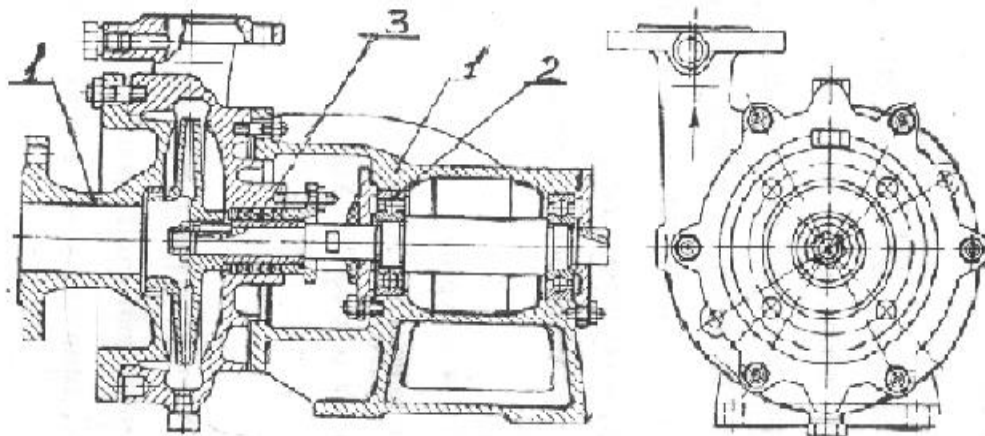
Общий вид центробежного насоса (гидравлической машины) в разрезе: 1) корпус насоса и его крышка (разъемная деталь). Детали заменяемые при текущем ремонте: 2) опорные подшипники; 3) уплотнительные кольца (манжеты)
